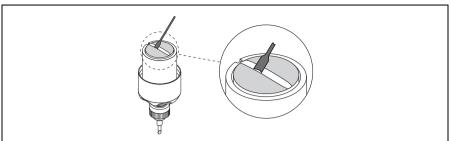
Enduire les surfaces de contact du capteur avec du produit de couplage
